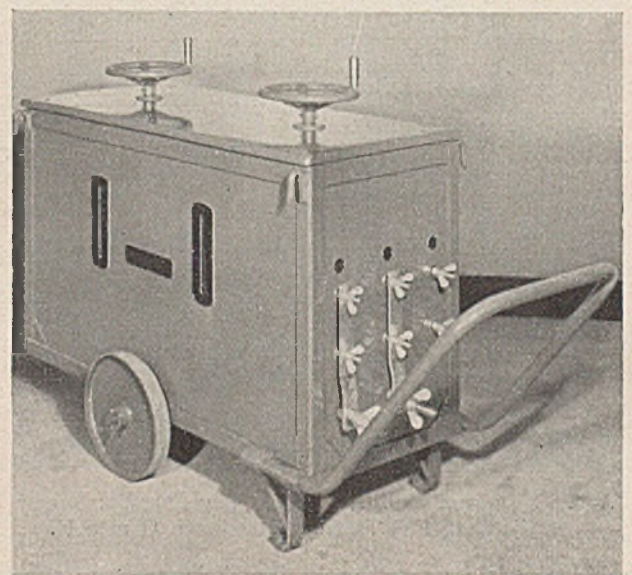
Schweißumspanner für 400 und 600 A für zwei voneinander unabhängige Schweißstellen der Arcos Gesellschaft für Schweißtechnik.
